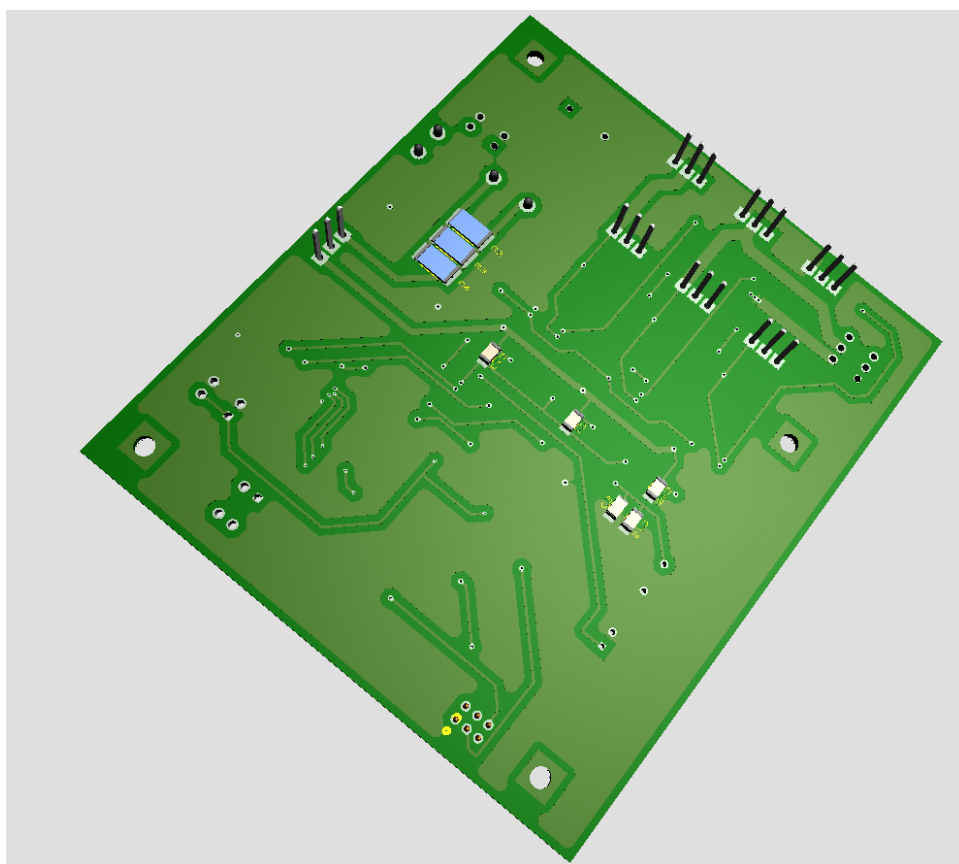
3D модель друкованої плати (вид знизу)
